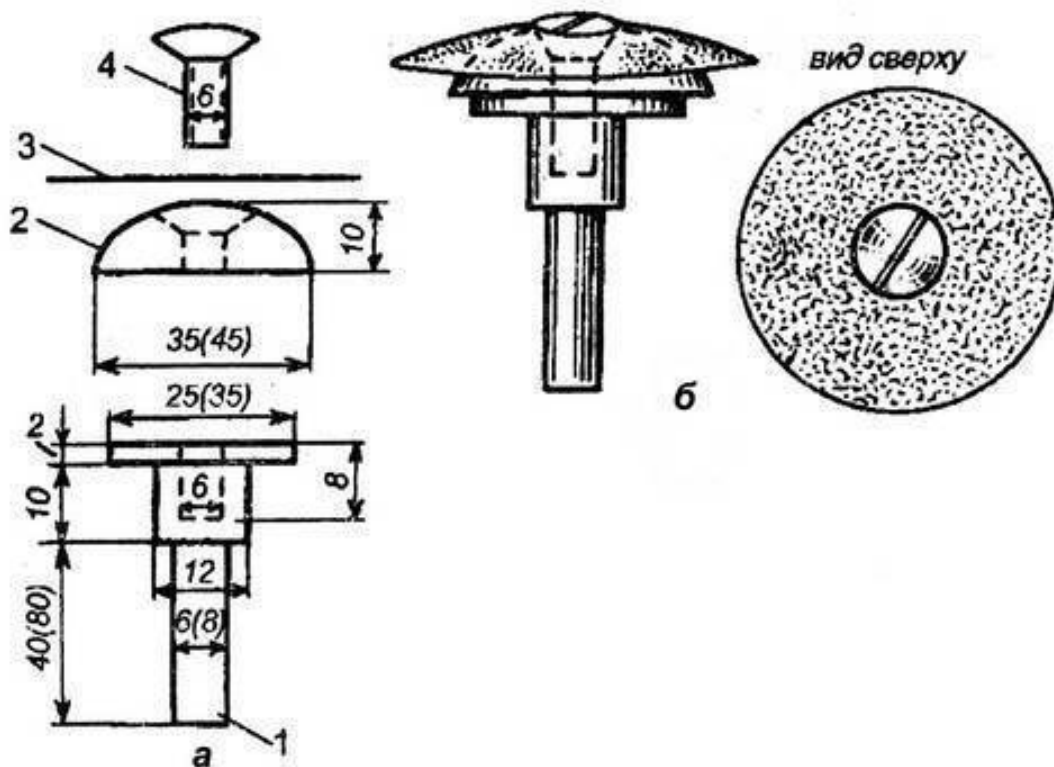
Полировальный грибок: а – детали (1 – ножка с площадкой, 2 – войлок; 3 – шкурка; 4 – скрепляющий винт); б – в собранном виде. Грибок с ножкой в 6 мм толщины, закрепленный в наконечнике бормашины, облегчает обработку узких, глубоких форм, объемов
